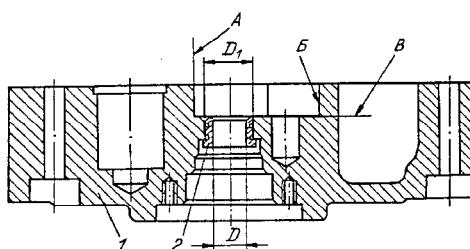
Корпус 2 нижний в сборе /рис. 129/
